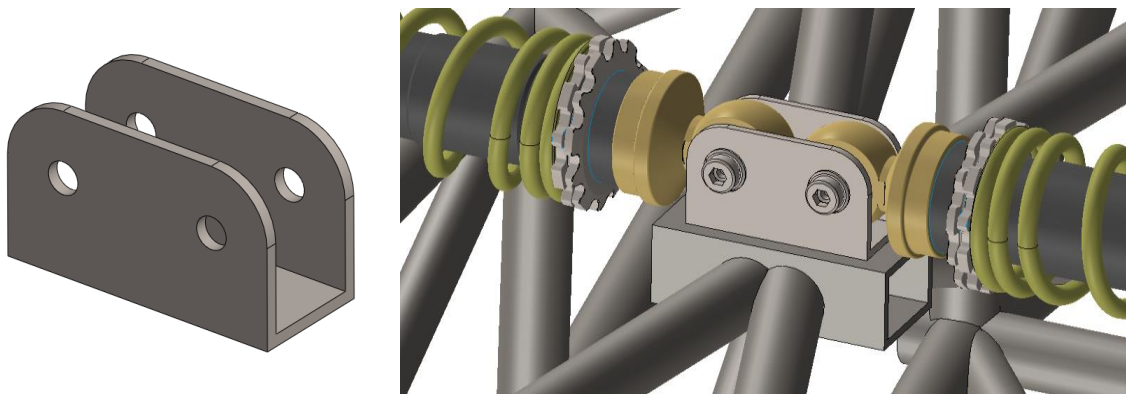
Diseño del soporte de balancín frontal (tipo 2)
